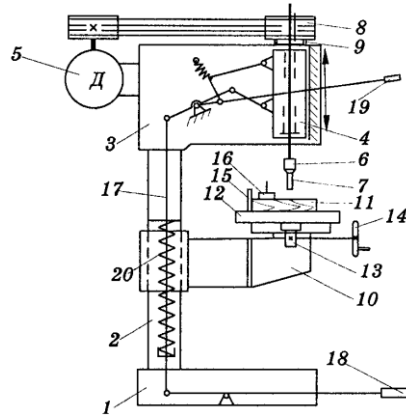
Вертикальний одношпиндельний свердлильний верстат: 1 – базувальна нижня плита; 2 – циліндрична колона; 3 – верхній кронштейн; 4 – свердлильний шпиндель; 5 – привод; 6 – патрон; 7 – свердло; 8 – приводний шків; 9 – підшипникова опора; 10 – кронштейн; 11 – заготівка; 12 – стіл; 13 – рейкова передача; 14 – маховичок; 15 – упор; 16 – затискач; 17 – важільна система; 18 – педаль; 19 – ручка; 20 – пружина
